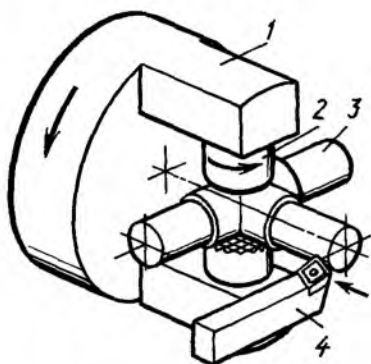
Поворотный патрон для обработки многоосных заготовок
